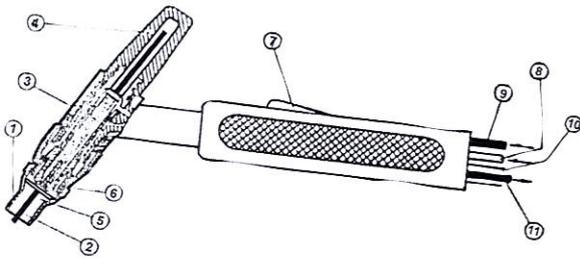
| Soldadura TIG (GTAW) con programación de corriente
